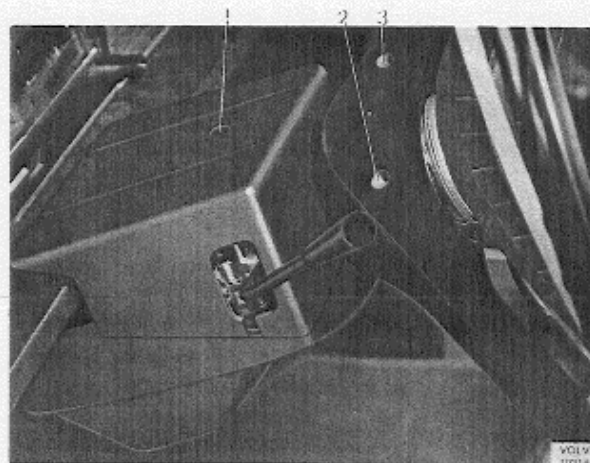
Befestigungsschrauben im Bereich der Lenksäule. Ausf. bis einschl. 1971
